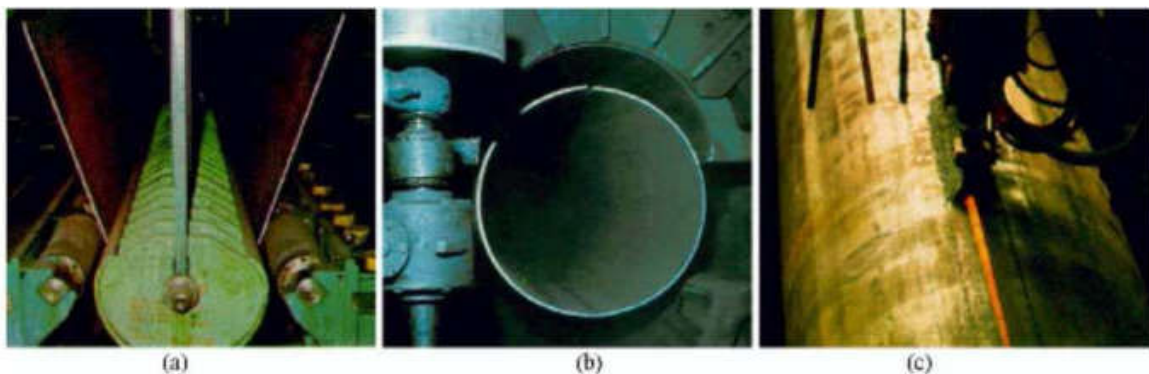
Fabrication des tubes soudés. (a) Formage en U, (b) formage en O et (c) soudage [14]
